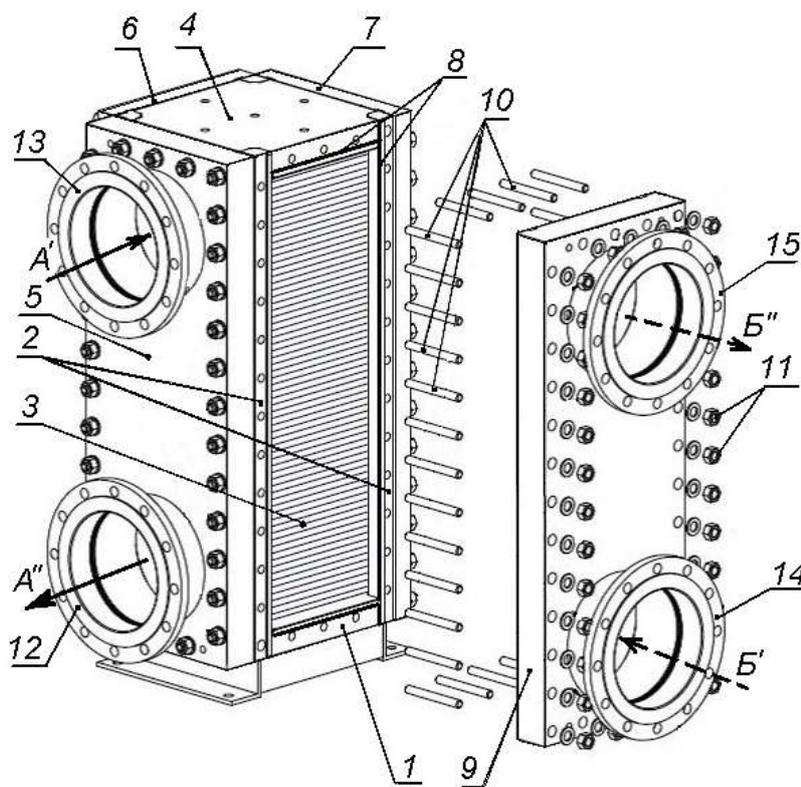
Общий вид компактного блочного разборного пластинчатого теплообменника марки Компаблок
